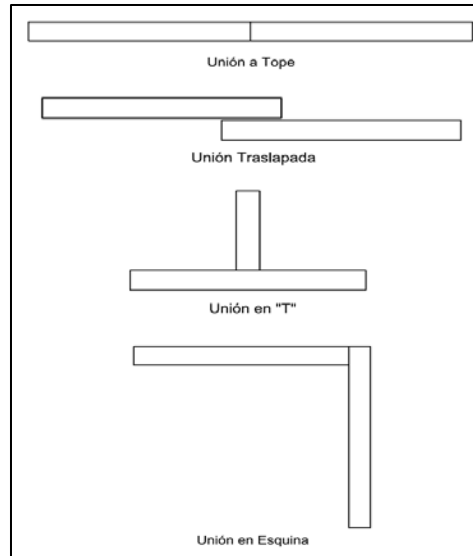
Diseños de uniones soldadas más comunes.
